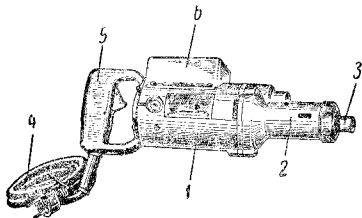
Электросверлилка И-90: 1 — корпус электродвигателя; 2 — корпус редуктора; 3 — шпиндель; 4 — рукоятка с выключателем; 5 — присоединительный кабель; 6 — фильтр подавления помех радиоприему.
